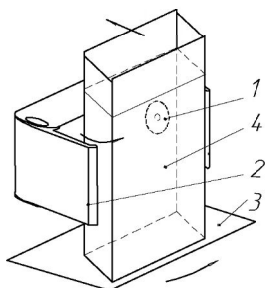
Формоутворення заготовки картонної пачки в карманному носії протягуванням по захвату: 1 - вакуумний захват, 2 - поворотні захвати, 3 - нижнє несуче дно, 4 - заготовка картонної пачки
